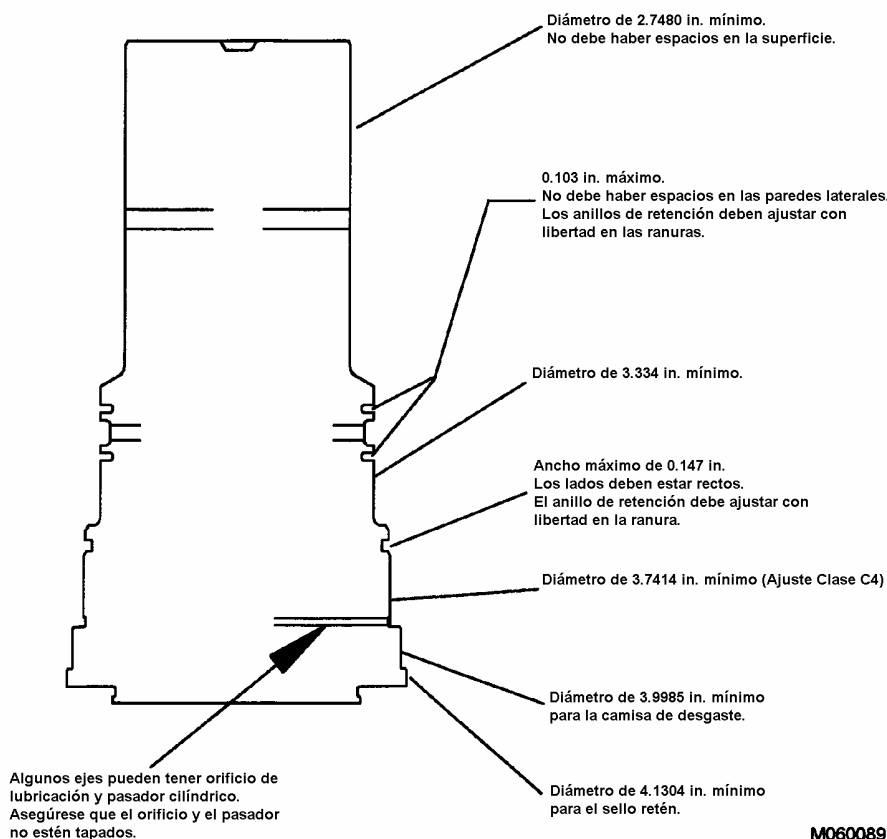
DIMENSIONES DE DESGASTE DEL CONJUNTO DEL EJE
